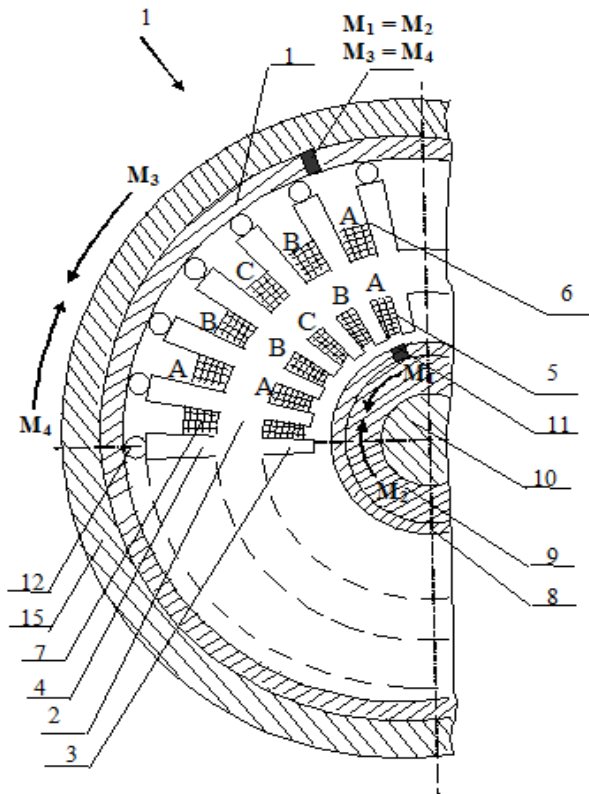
Двухроторный шаговый асинхронный двигатель:
